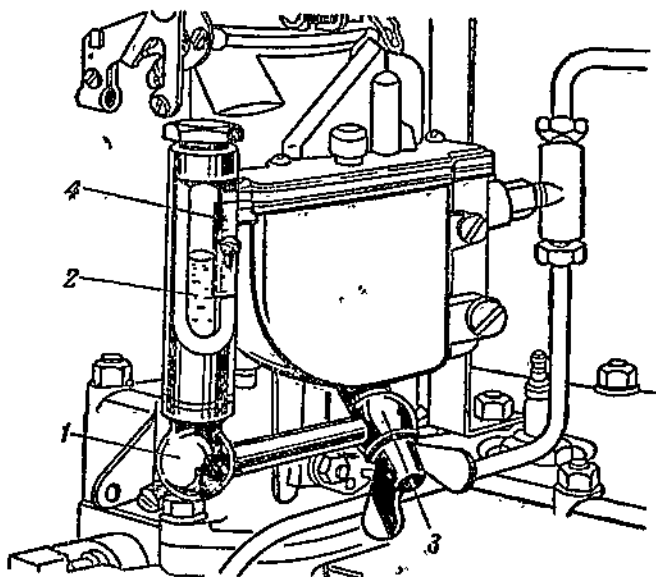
Приспособление для проверки уровня топлива в поплавковой камере без разборки карбюратора
